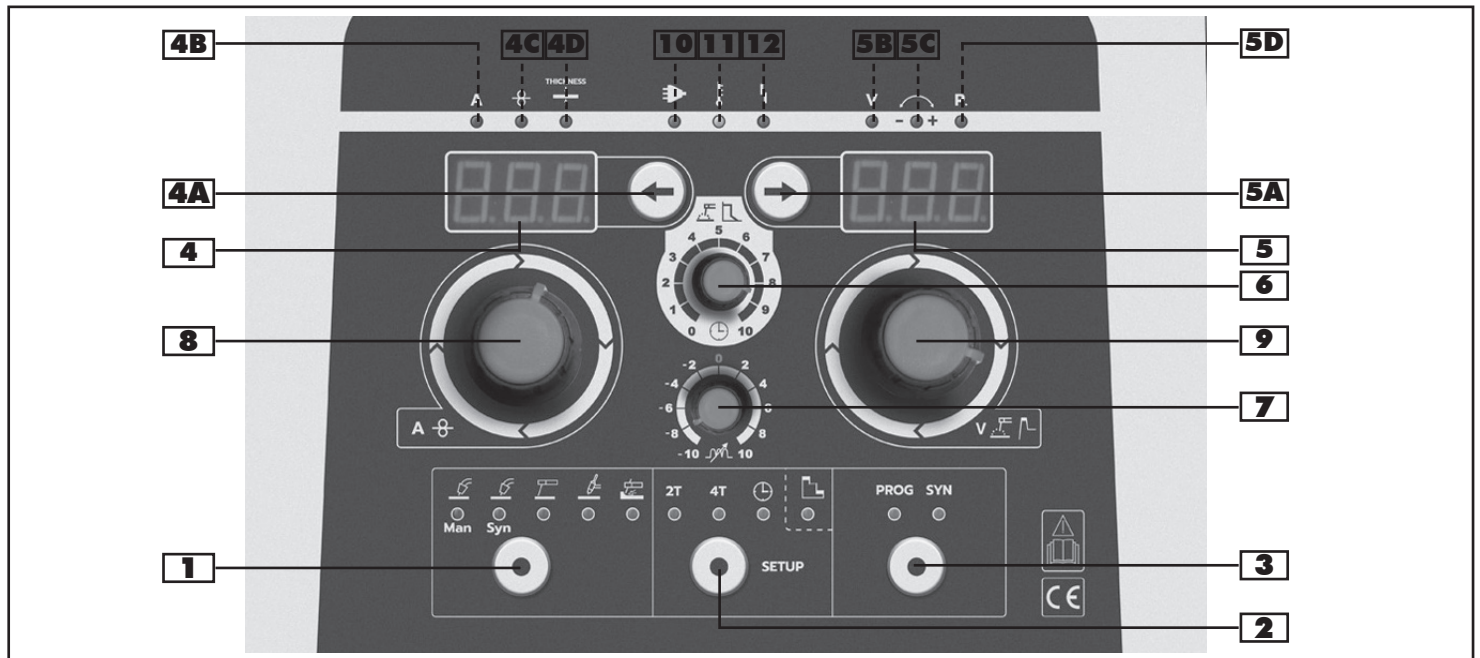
Panel de control del Alimentador y de la soldadora compacta - Panel A
